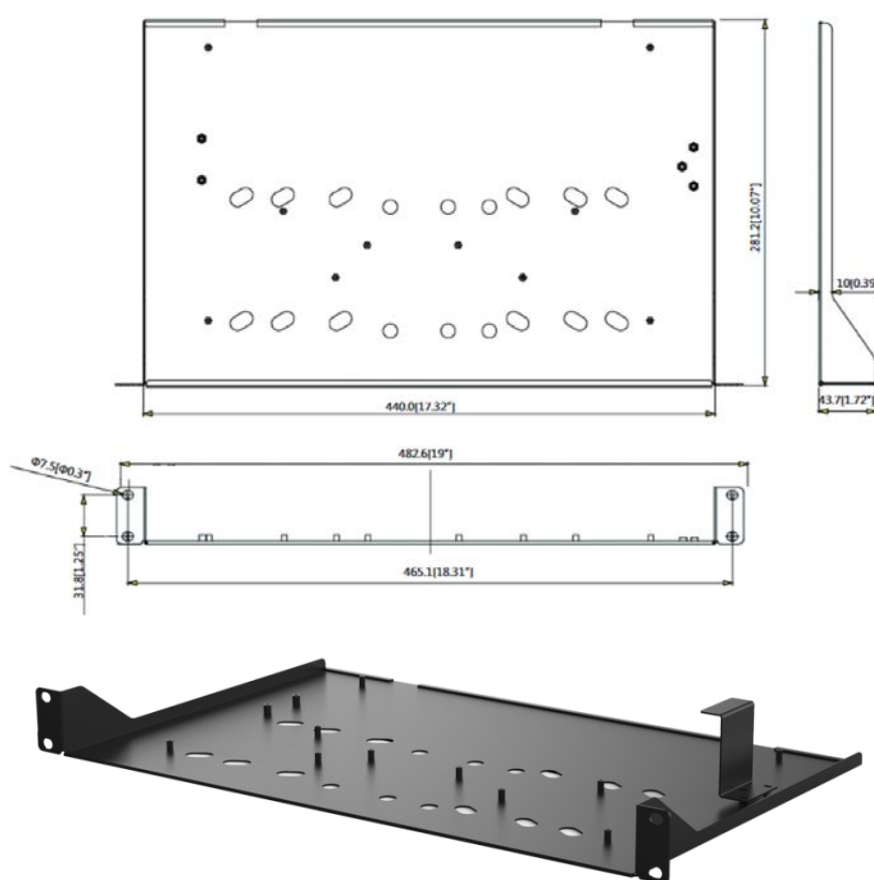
Внешний вид и габариты BOLID BR-111
